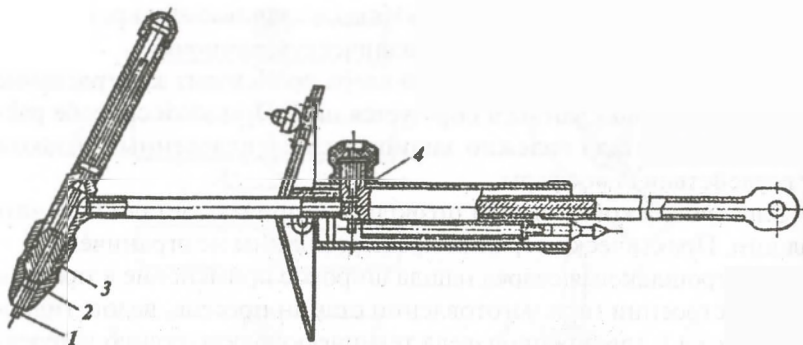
Горелка для сварки в среде защитного газа неплавящимся электродом
